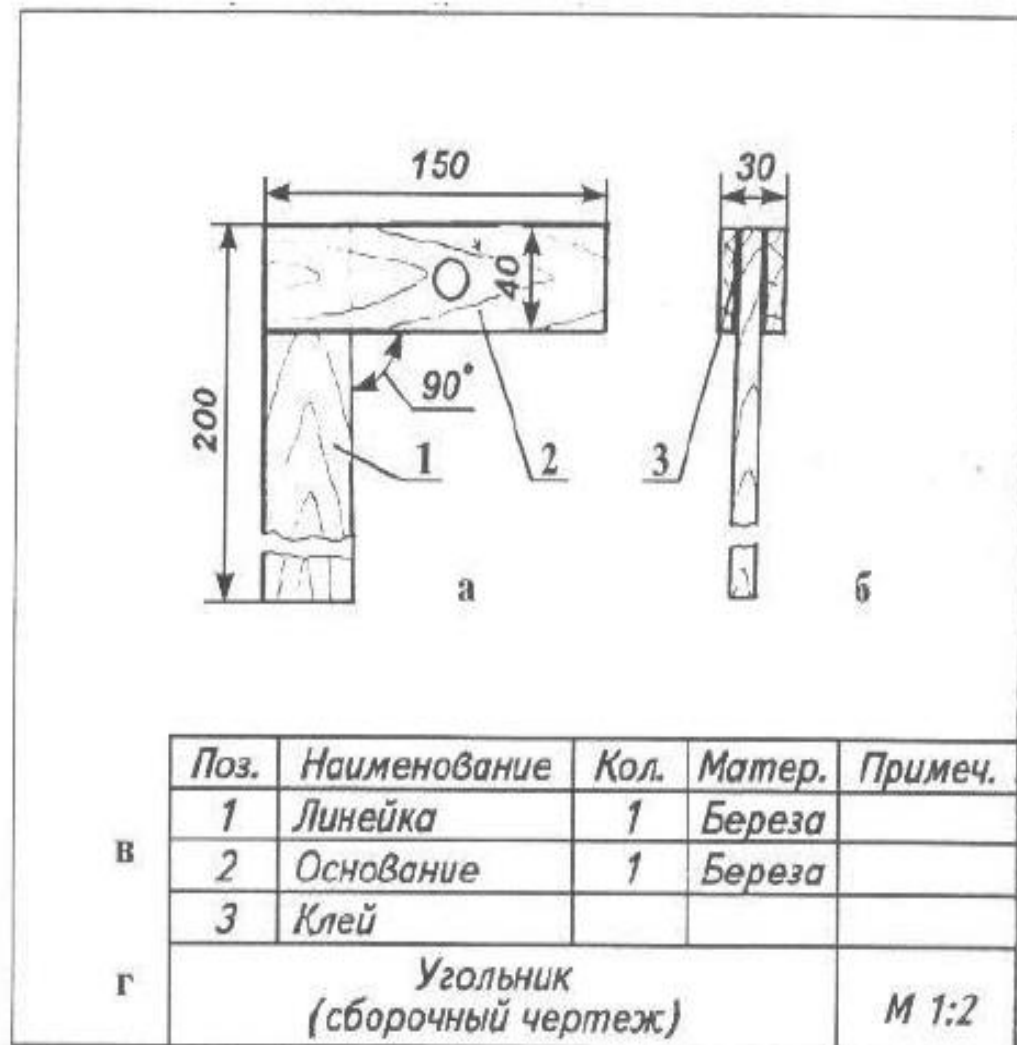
Сборочный чертеж угольника: а — главный вид; б — вид слева; в — спецификация; г — основная надпись
